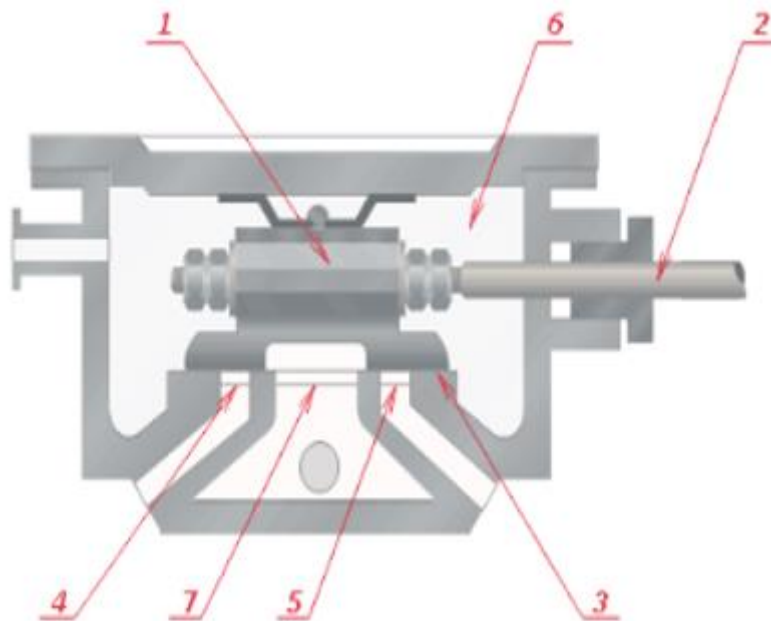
Золотник: 1 – перевернута коробка; 2 – тяга; 3 – золотникове дзеркало; 4 та 5 – прямокутні вікна; 6 – замкнутий простір; 7 – порожнина, спільною з атмосферою чи конденсатором
